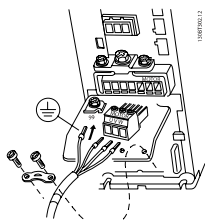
Motoranschluss für A1, A2 und A3
